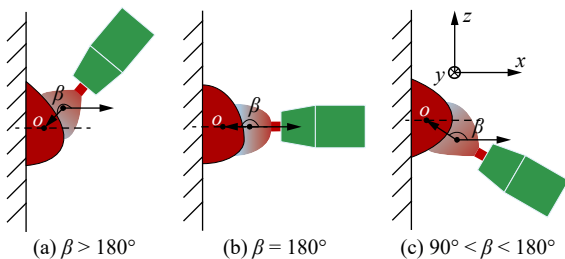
焊枪倾斜角度对悬空焊缝成形影响
